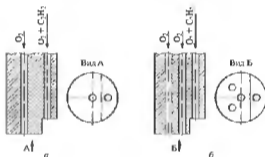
Схемы мунштуков для резки металла малой толщины.
